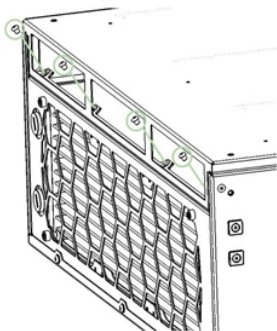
Извлечение винтов фиксации нижней задней крышки с корпусом
